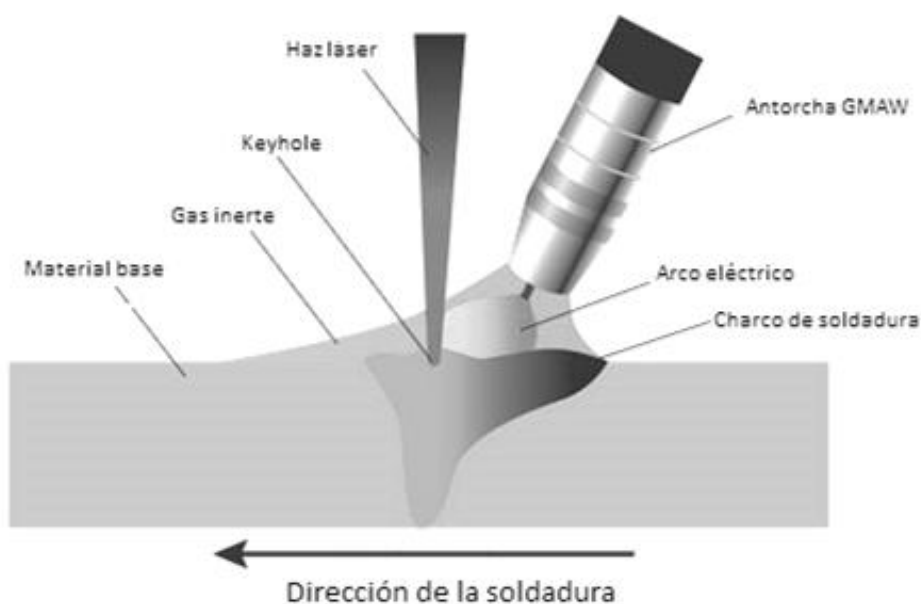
Esquema del proceso de soldadura HLAW [23].
